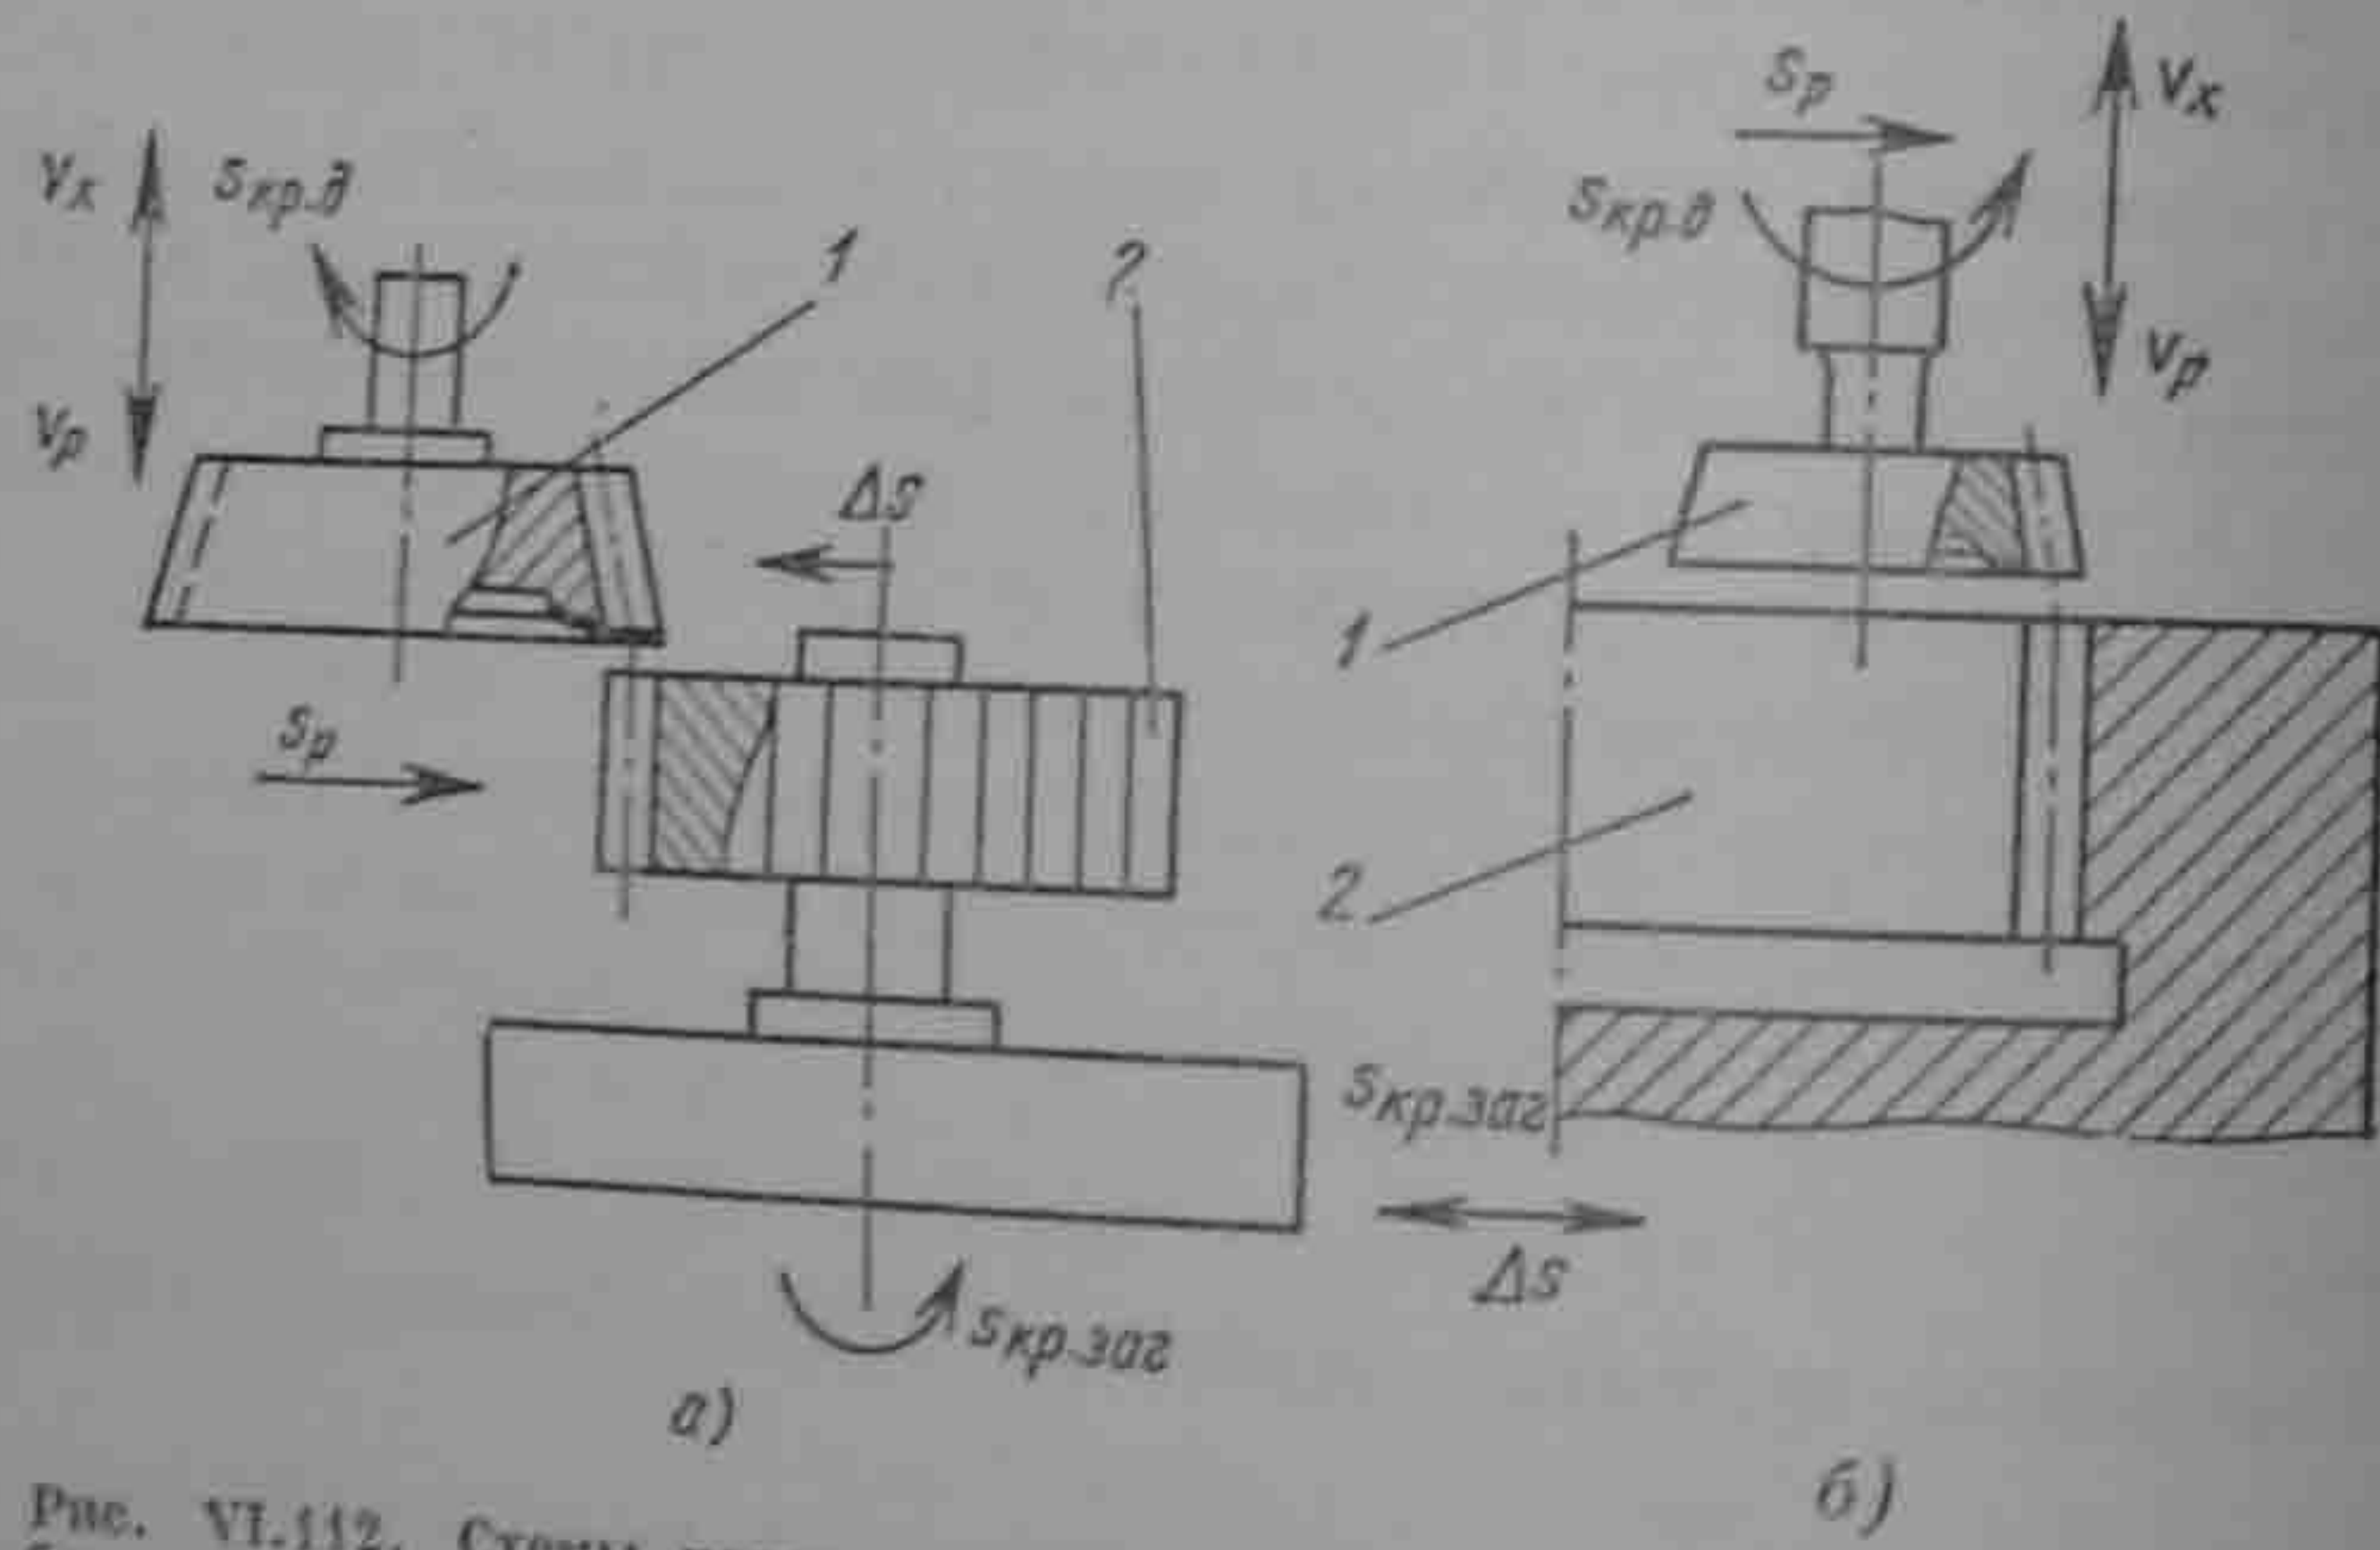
Схемы нарезания цилиндрических колес с прямыми зубьями внешнего (а) и внутреннего (б) зацеплений на зубодолбежном станке: 1 — долбьяк; 2 — нарезаемое колесо
